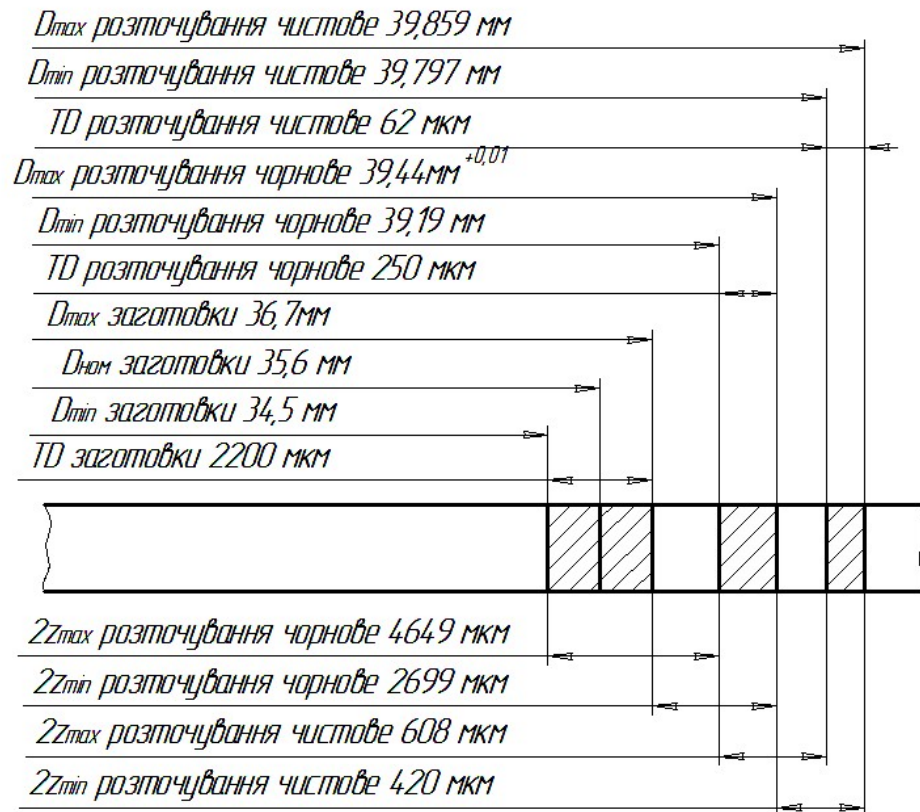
Схема розташовування припусків і допусків на оброблення
